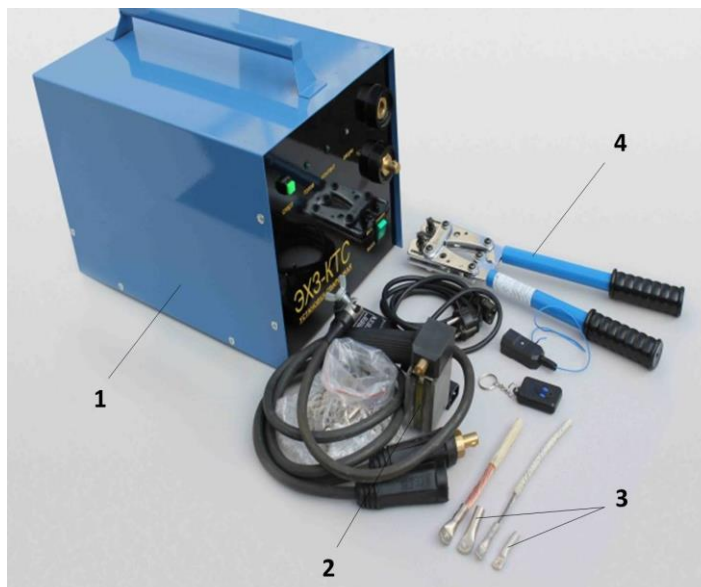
Комплект оборудования ЭХЗ-КТС для конденсаторной сварки:
